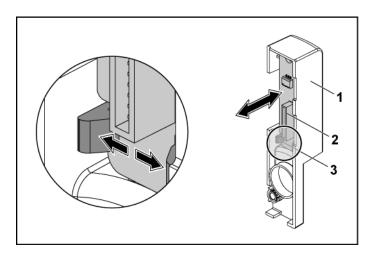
Frontblenden-Baugruppe entfernen und installieren
